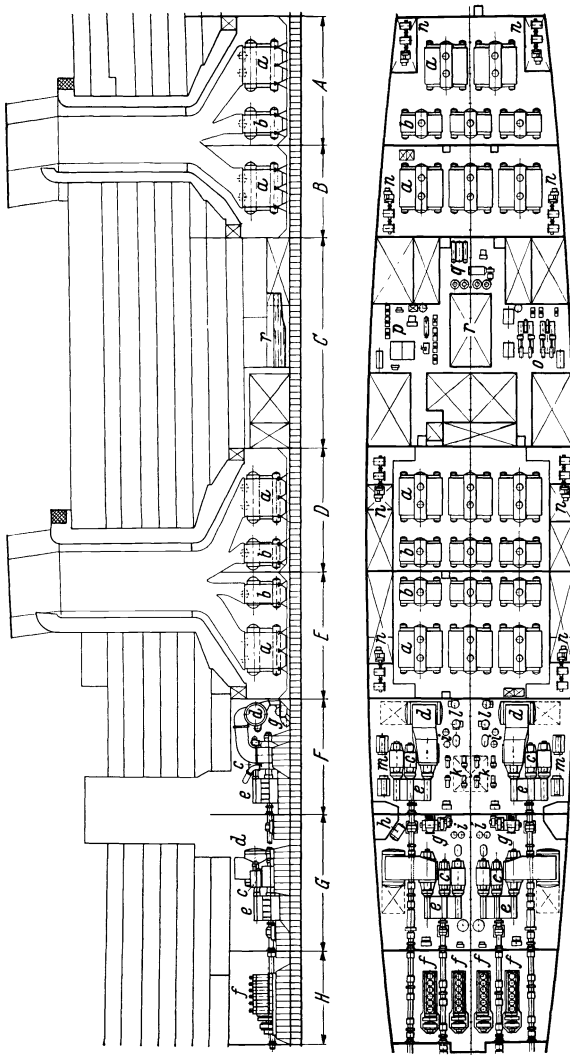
Antriebsanlage des Schnelldampfers „Bremen“. A Kesselraum I, B Kesselraum II, C Kühlmaschinen- und Pumpenraum, D Kesselraum III, E Kesselraum IV, F Turbinenraum I, G Turbinenraum II, H Hilfsmaschinenraum, a Doppelender-Wasserrohrkessel, b Einender-Wasserrohrkessel, c Hauptturbinen, d Hauptkondensatoren, e Getriebe, f Diesel-Generatoren, g Hauptkühlwasserpumpen, h Hilfskondensatoren, i Kondensatpumpen, k Hauptseparatoren, l Speisewasservorwärmer, m Verdampfer, n Kesselraumgebläse, o Kühlmaschinen, p Kühlanlage, r Schwimmbock.
